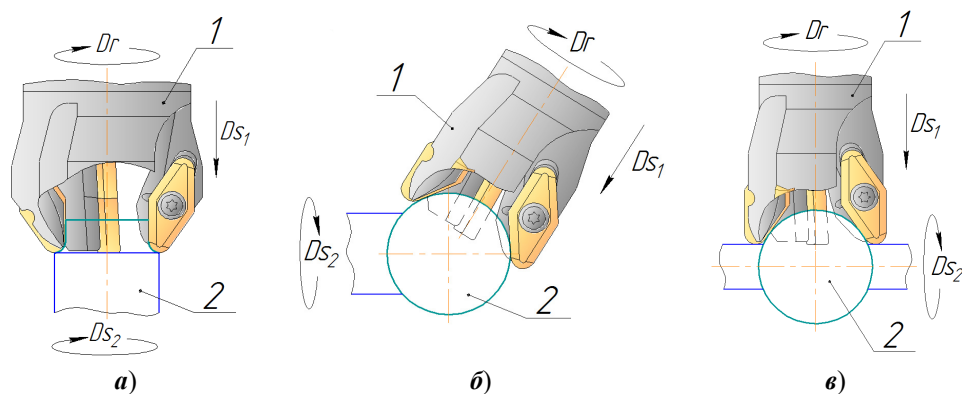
Схемы обработки охватывающими фрезами (зенкерами) поверхностей:
